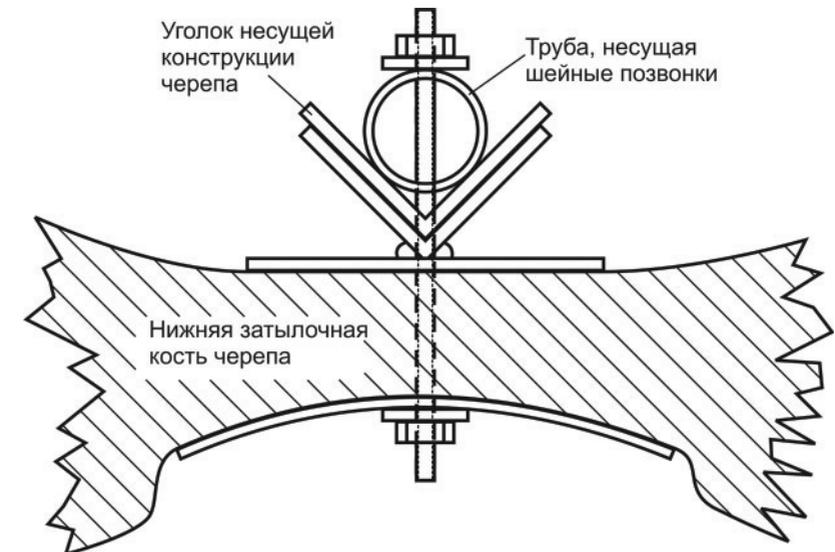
Схема крепления несущей конструкции к затылочной кости черепа
